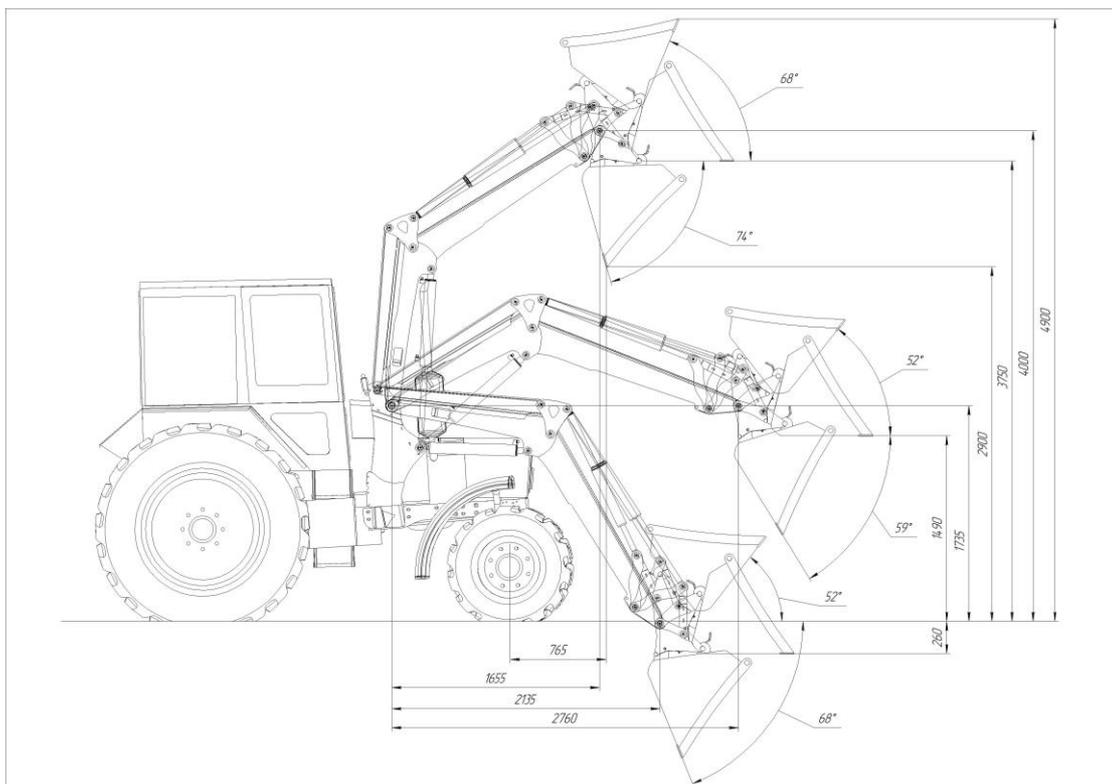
Габаритные размеры погрузчика Универсал Robust
